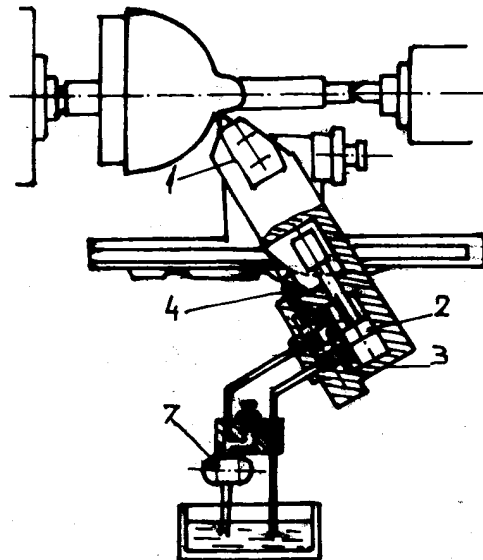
Schéma hydraulického kopírovacího systému pro obecné tvary
